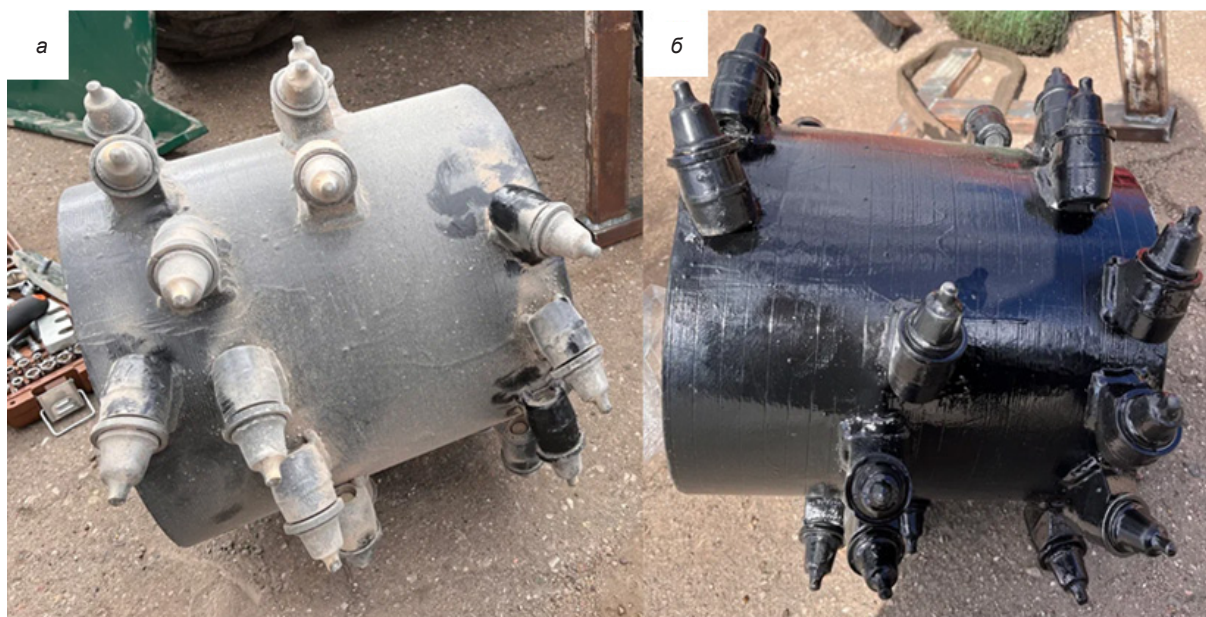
Сменные фрезерные барабаны: а – фрезерный барабан № 1; б – фрезерный барабан № 2
